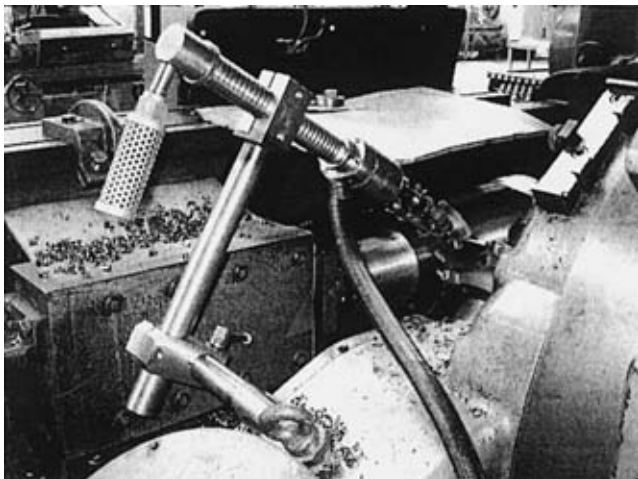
Вихревая подготовка и подача воздушно-жидкостного аэрозоля COTC при обработке ротора винтового компрессора
